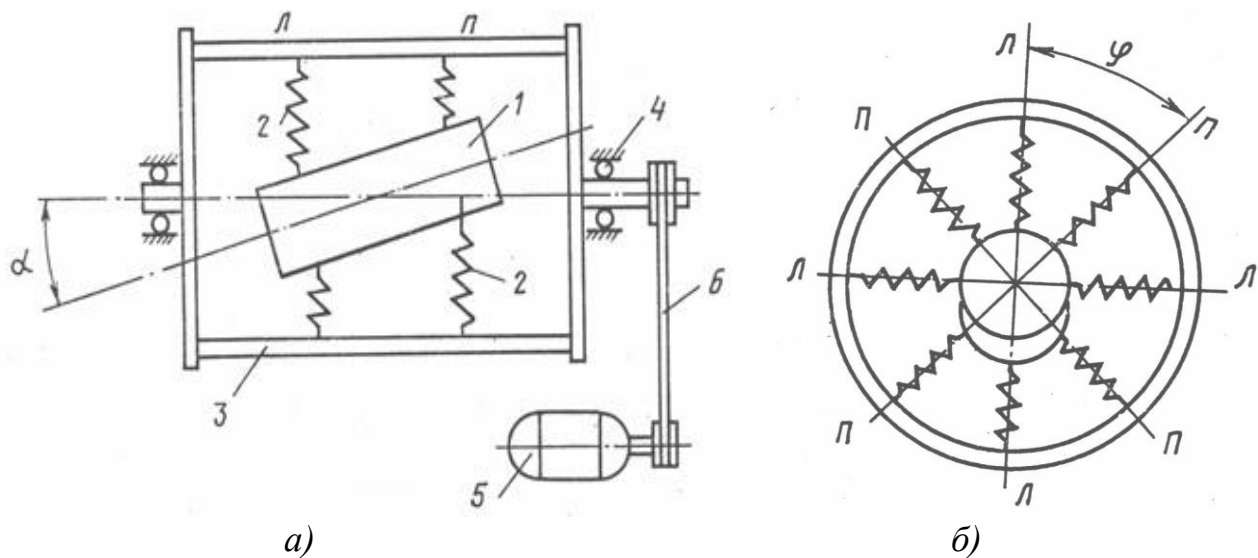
Схема машины для виброгалтовочной обработки деталей - а); схема расположения пружин его подвески относительно друг друга - б)
